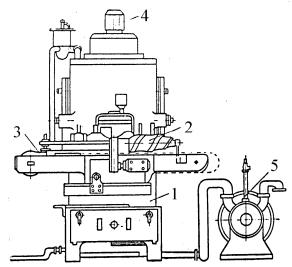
Автоматическая вакуум-закаточная машина 3B-7: 1 — станина; 2 — загрузочное устройство; 3 — разгрузочное устройство; 4 — привод; 5 — вакуум-насос
